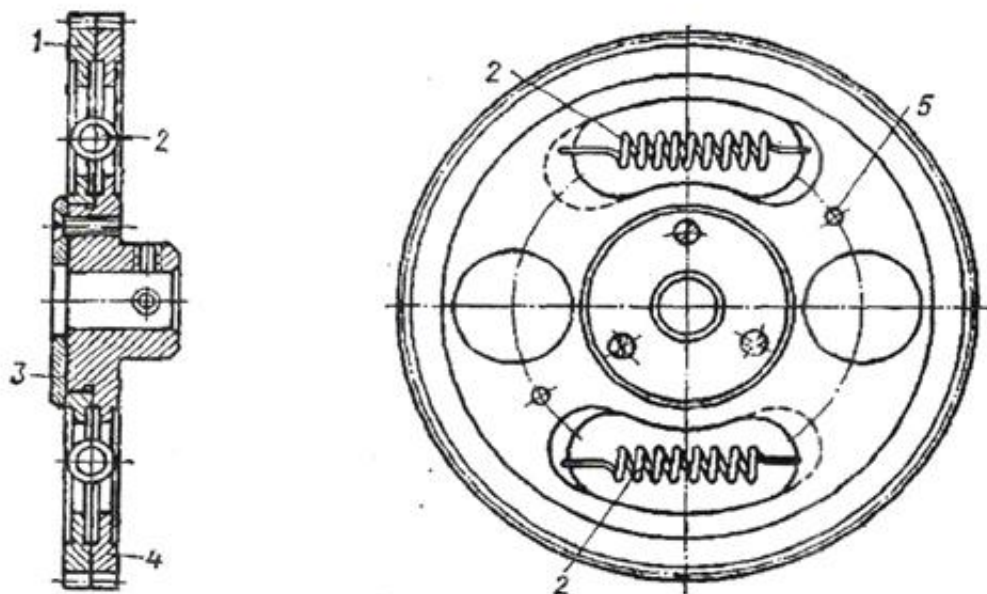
Колесо с устройством выборки бокового зазора между зубьями
